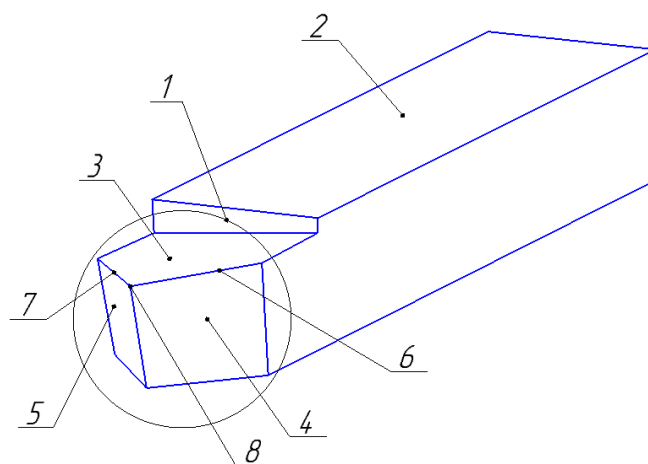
Режущий инструмент (токарный резец) и его элементы:
